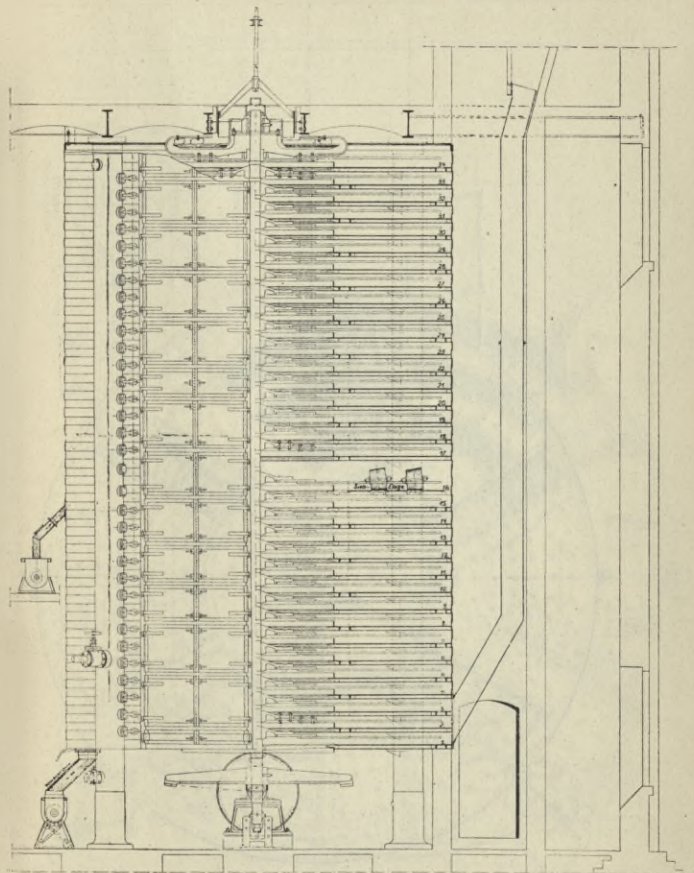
a. Tellerdöckner, Aufriß. Ausführung der Maschinenfabrik
